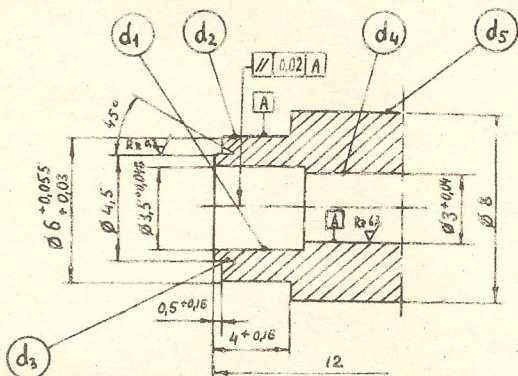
Фрагмент конструкции обрабатываемой детали
